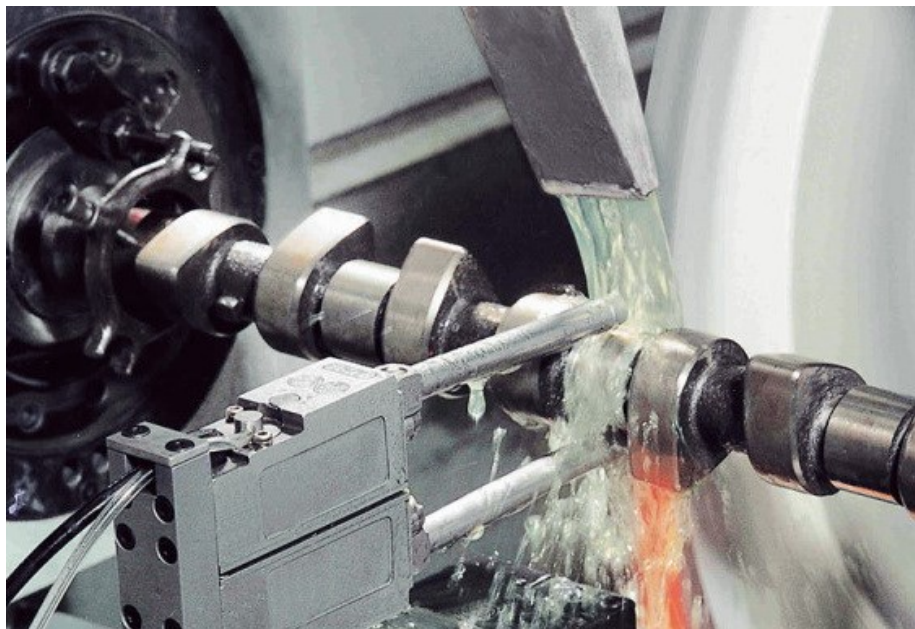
Пример обработки на станке с ЧПУ, содержащий сервопривод
